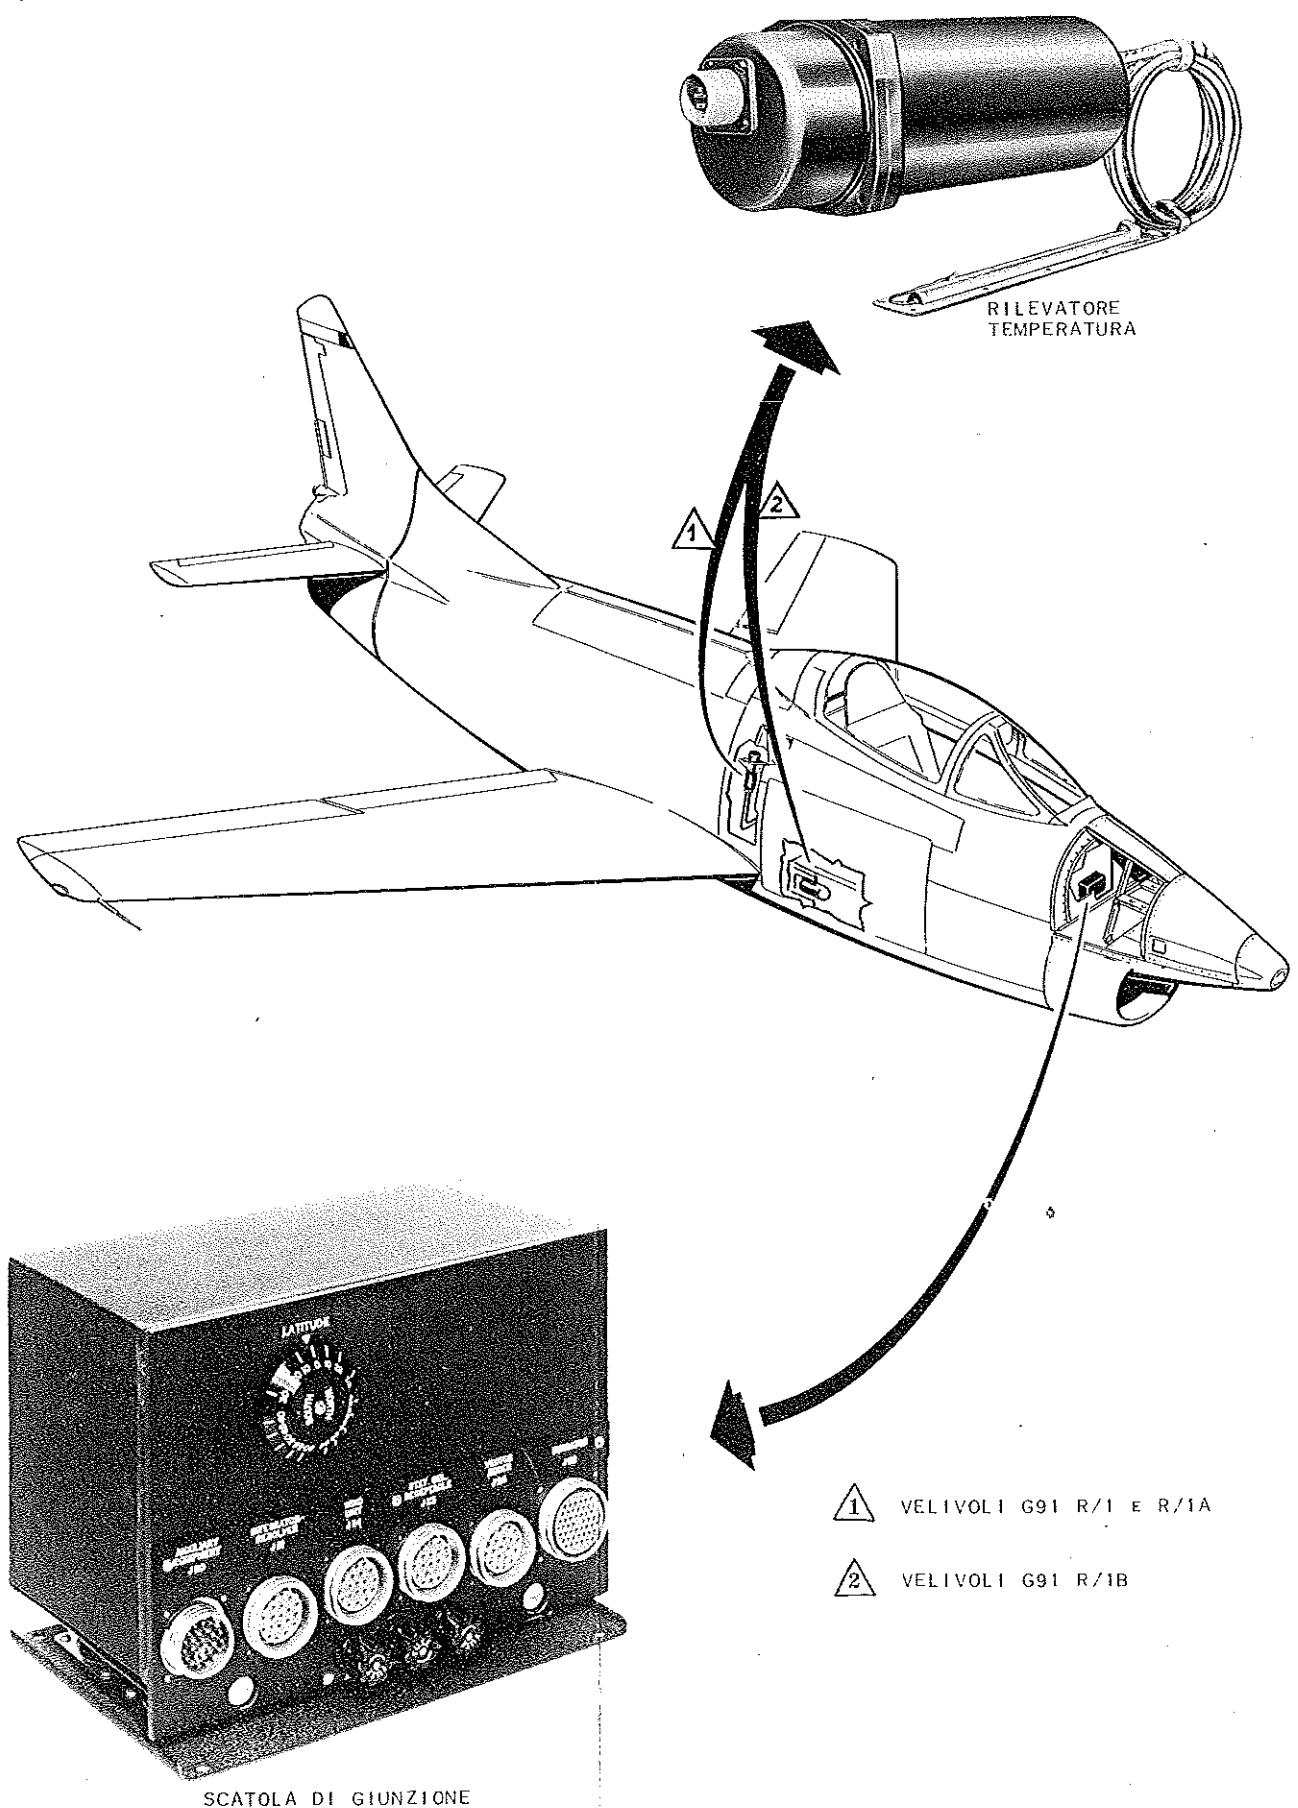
DISLOCAZIONE APPARECCHIATURE IMPIANTO DI NAVIGAZIONE
